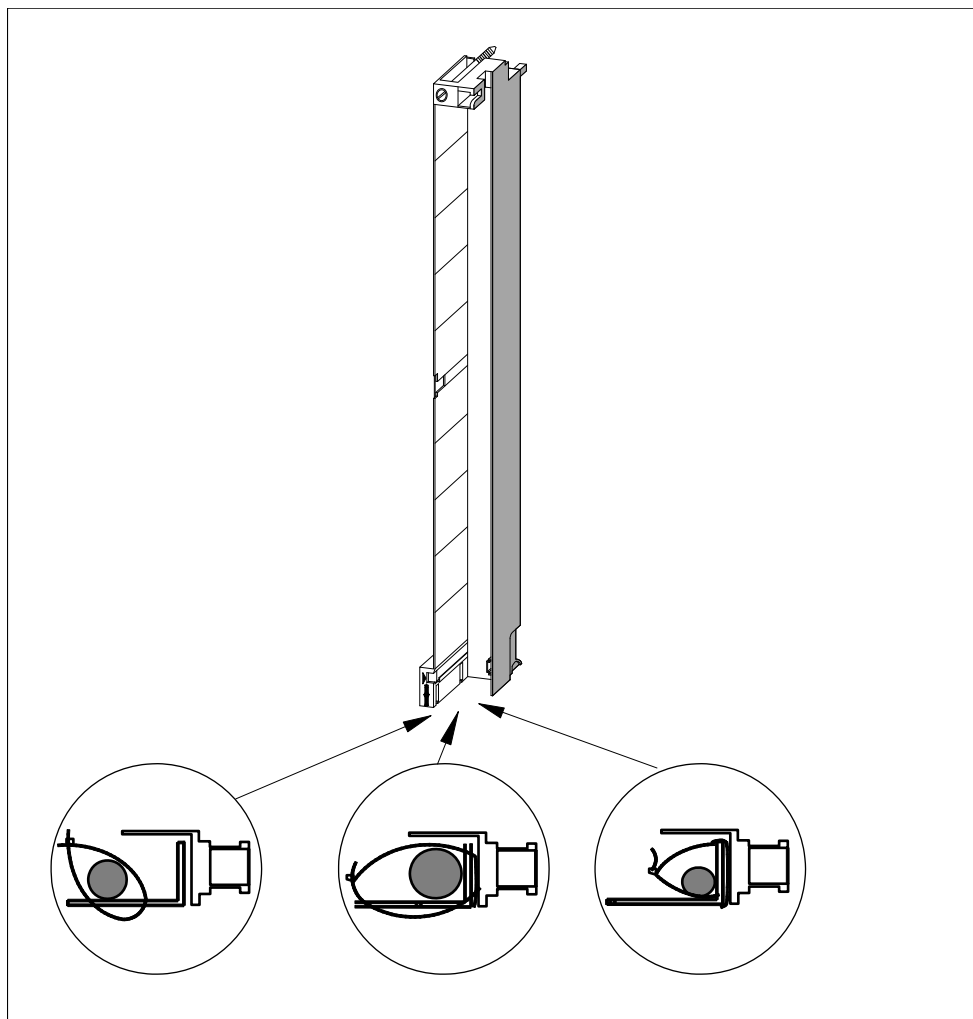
Установка компенсатора натяжения (вид снизу)
